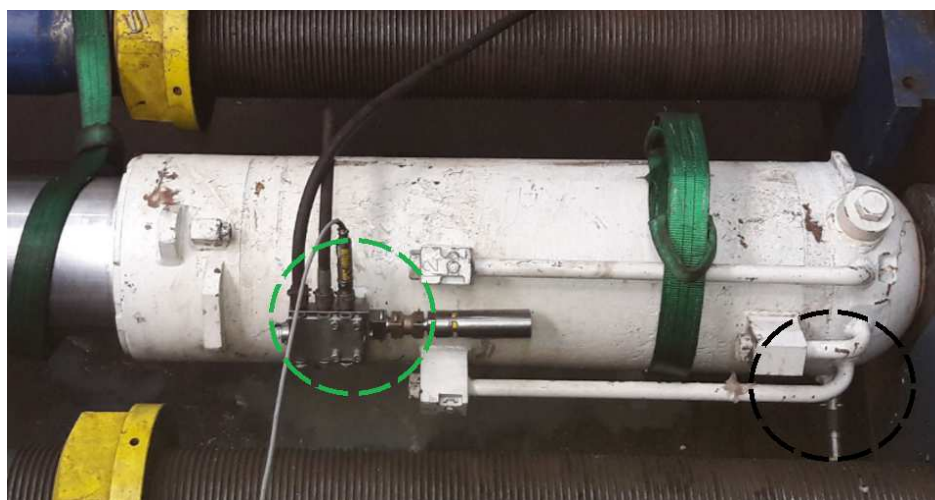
Wariant pierwszy połączenia elementów hydraulicznych w układzie zabezpieczającym stojak (źródło własne)
